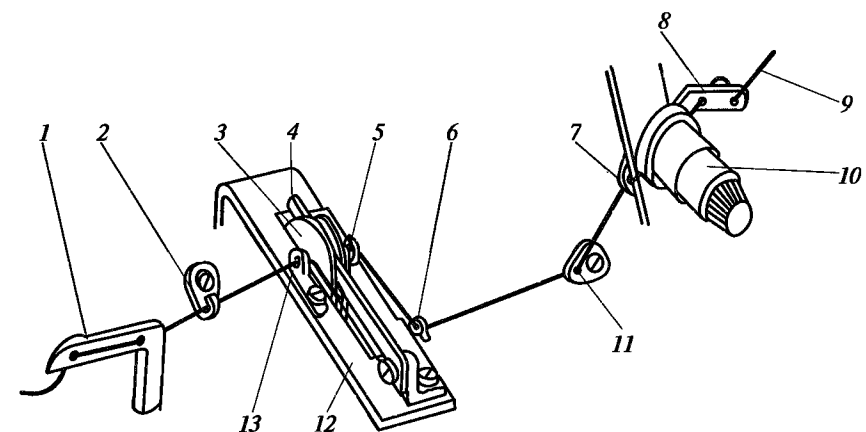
Схема заправки нитки петлителя в швейной машине класса 1276
